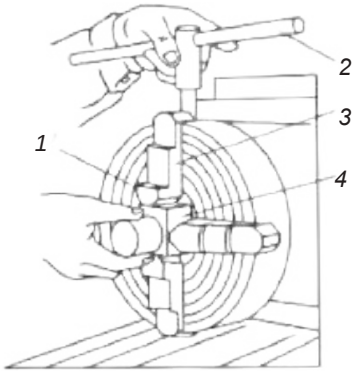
Попереднє закріплення та вивірка заготовки за кільцевими рисками: 1 — кільцеві риси; 2 — токарний ключ; 3 — кулачки; 4 — заготовка
